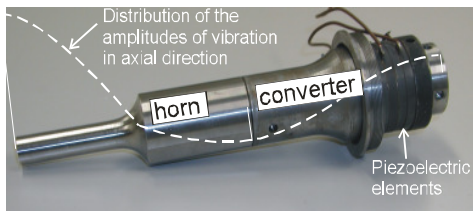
Ultraschallerzeuger mit Transformationsstück (Horn)
